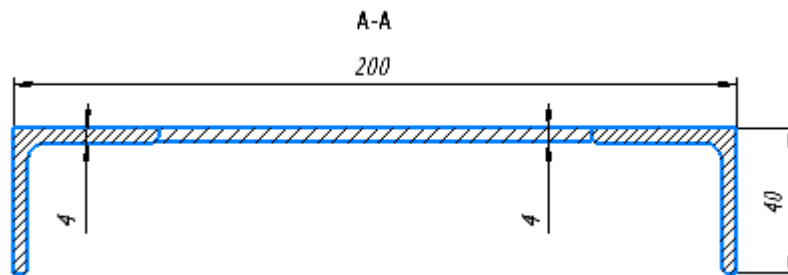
Ступень металлической лестницы ФЮРА.20000.00001
